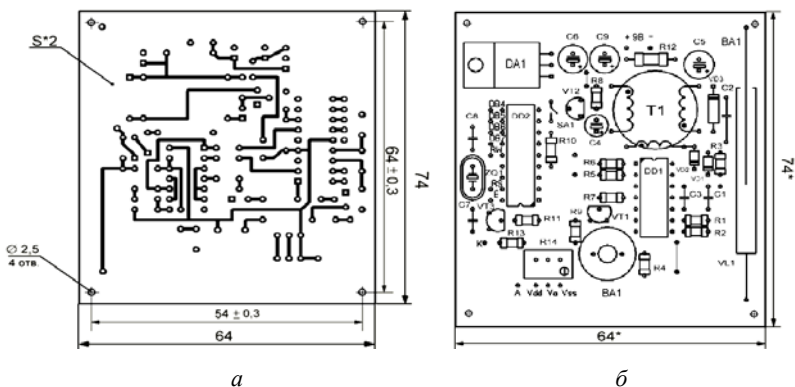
Эскизы: печатной платы (а); сборочного чертеж платы (б)
